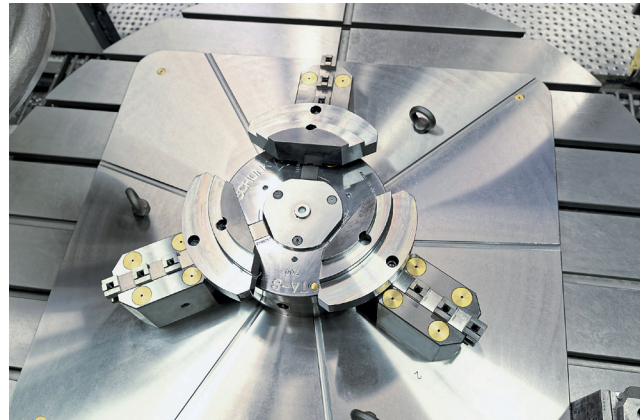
ROTA-S flex позволяет работать с заготовками любых диаметров. Это универсальный ручной токарный патрон
